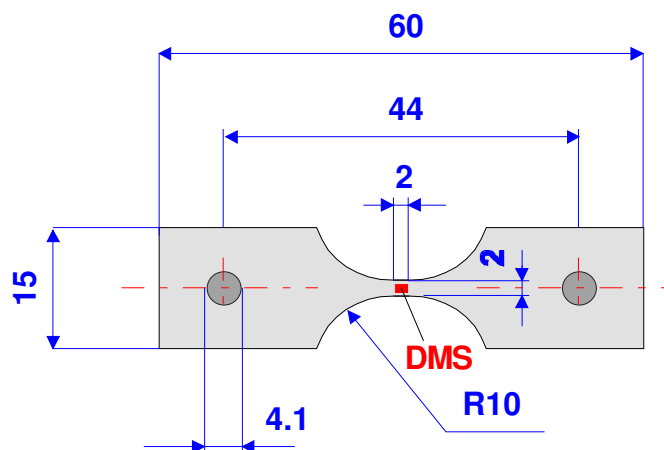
Geometrie der für die Dehnungsfeldmessung verwendeten Proben (ca. 1 mm dick)
